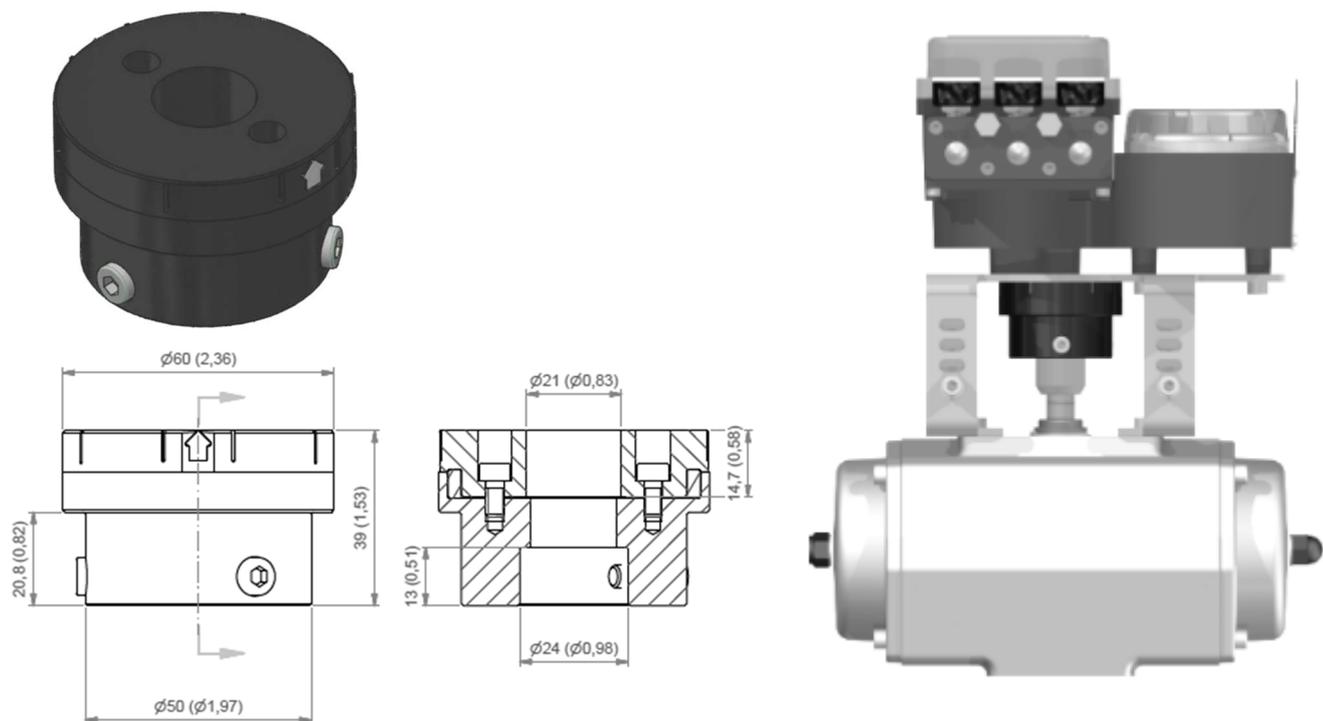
Dimensiones y montaje del imán giratorio.
